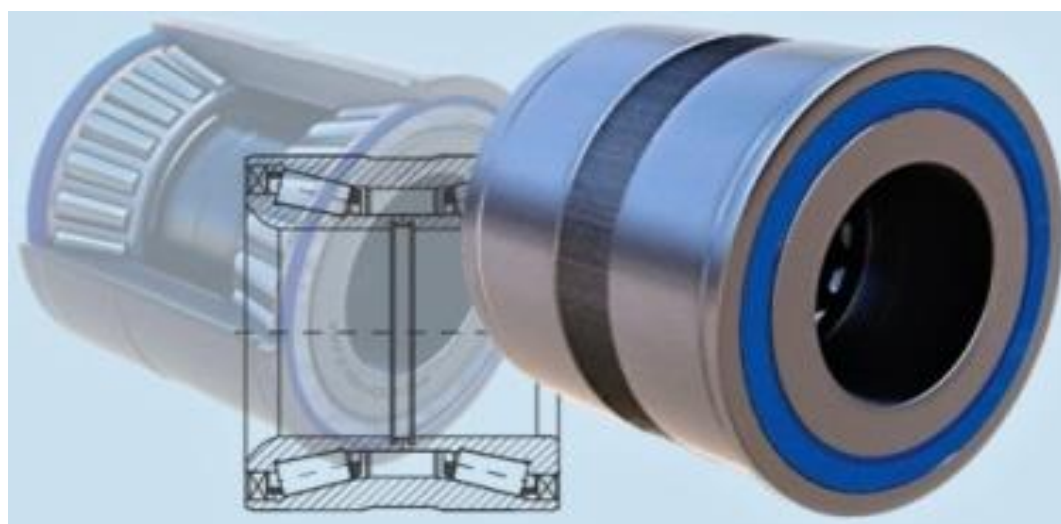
Підшипниковий вузол маточини HWT (HUB WHEEL TRUCK)
